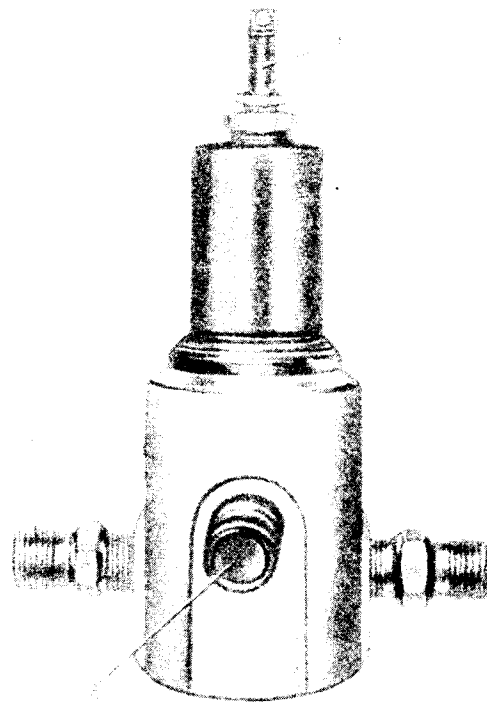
Напорный золотник: I - регулировочный винт; а - отвод; б - подвод
